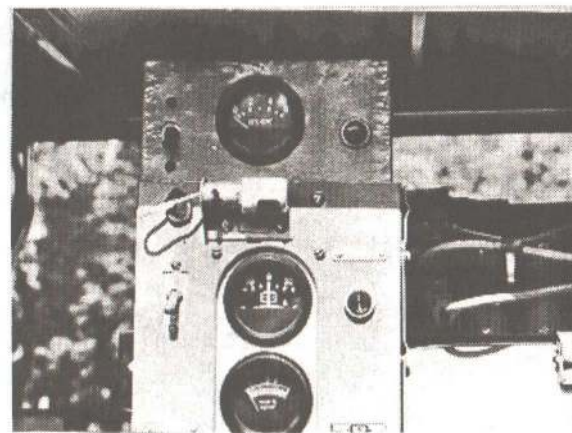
Вид на органы управления газовым оборудованием сварочной установки
